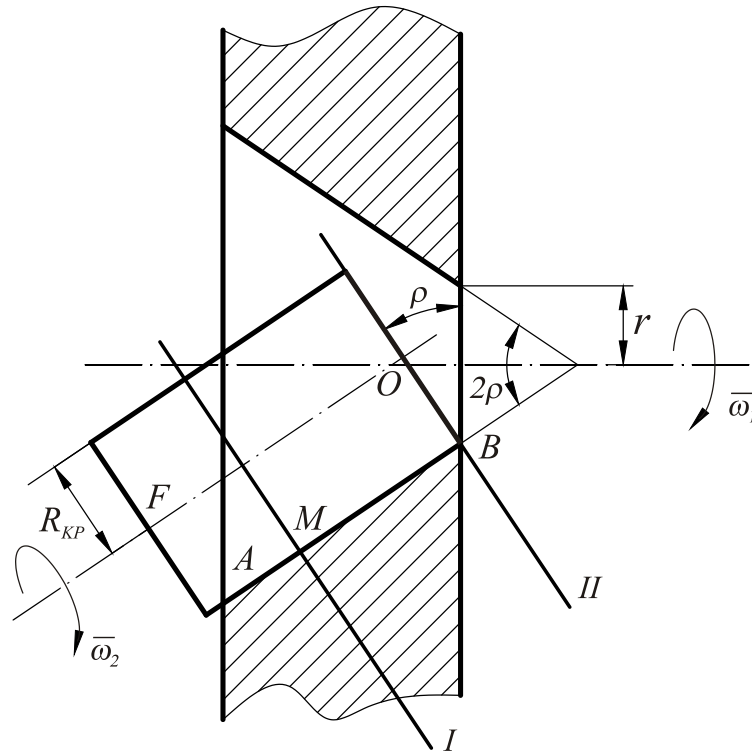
Визначення діаметра циліндричного кола при шліфуванні конічної поверхні
